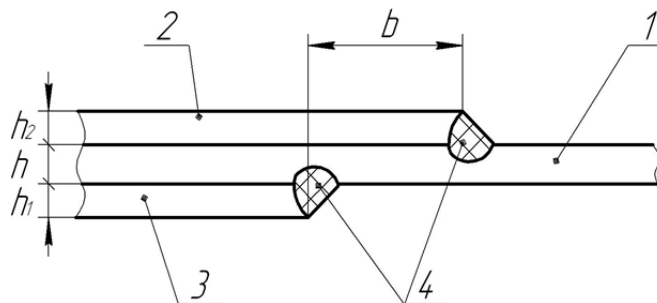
Схема сварки элементов усиления рамы (в сечении): 1 - металл рамы; 2,3 - металл элементов усиления; 4 - сварочные швы
